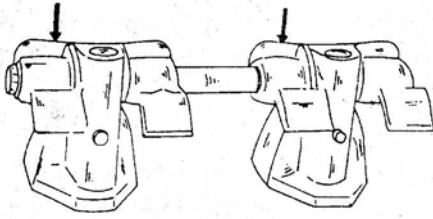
Крепление проволочных скоб на опорах рычагов коромысел.
